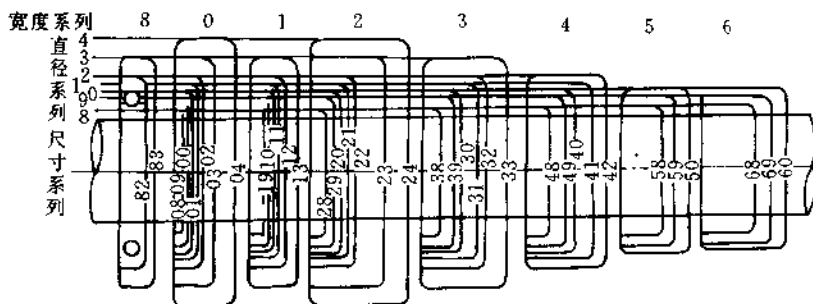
向心轴承的尺寸系列示意图(圆锥滚子轴承除外)
